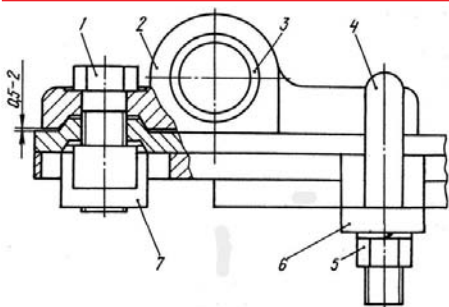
Крепление ушка рессоры: 1 — болт; 2 — ушко; 3 — втулка ушка; 4 — стремянка; 5 — гайка; 6 — накладка; 7 — гайка
